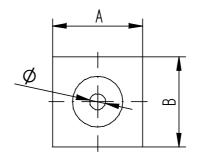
SKINTOP® CUBE MODULE ASI BUS
